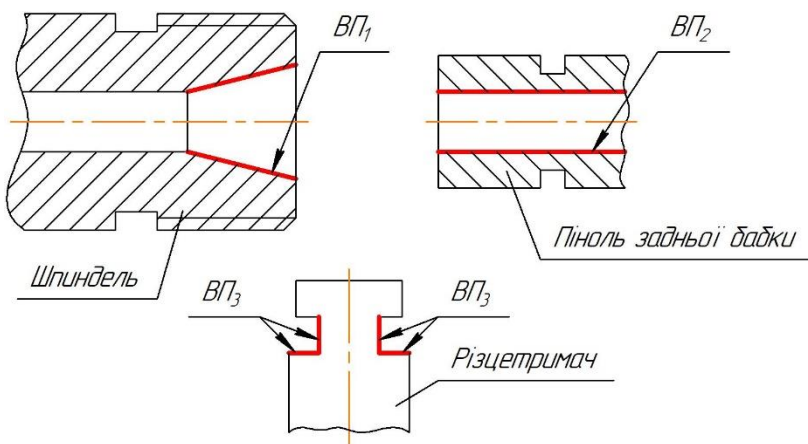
Виконавчі поверхні під час оброблення вала в центрах
